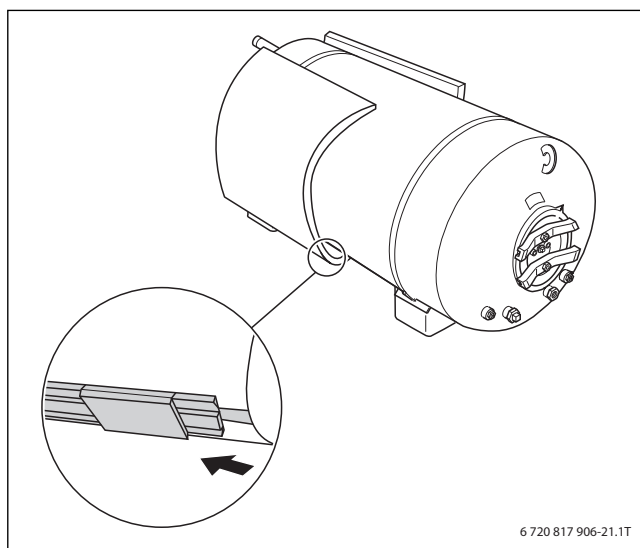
Položení segmentu tepelné izolace pod zásobník
